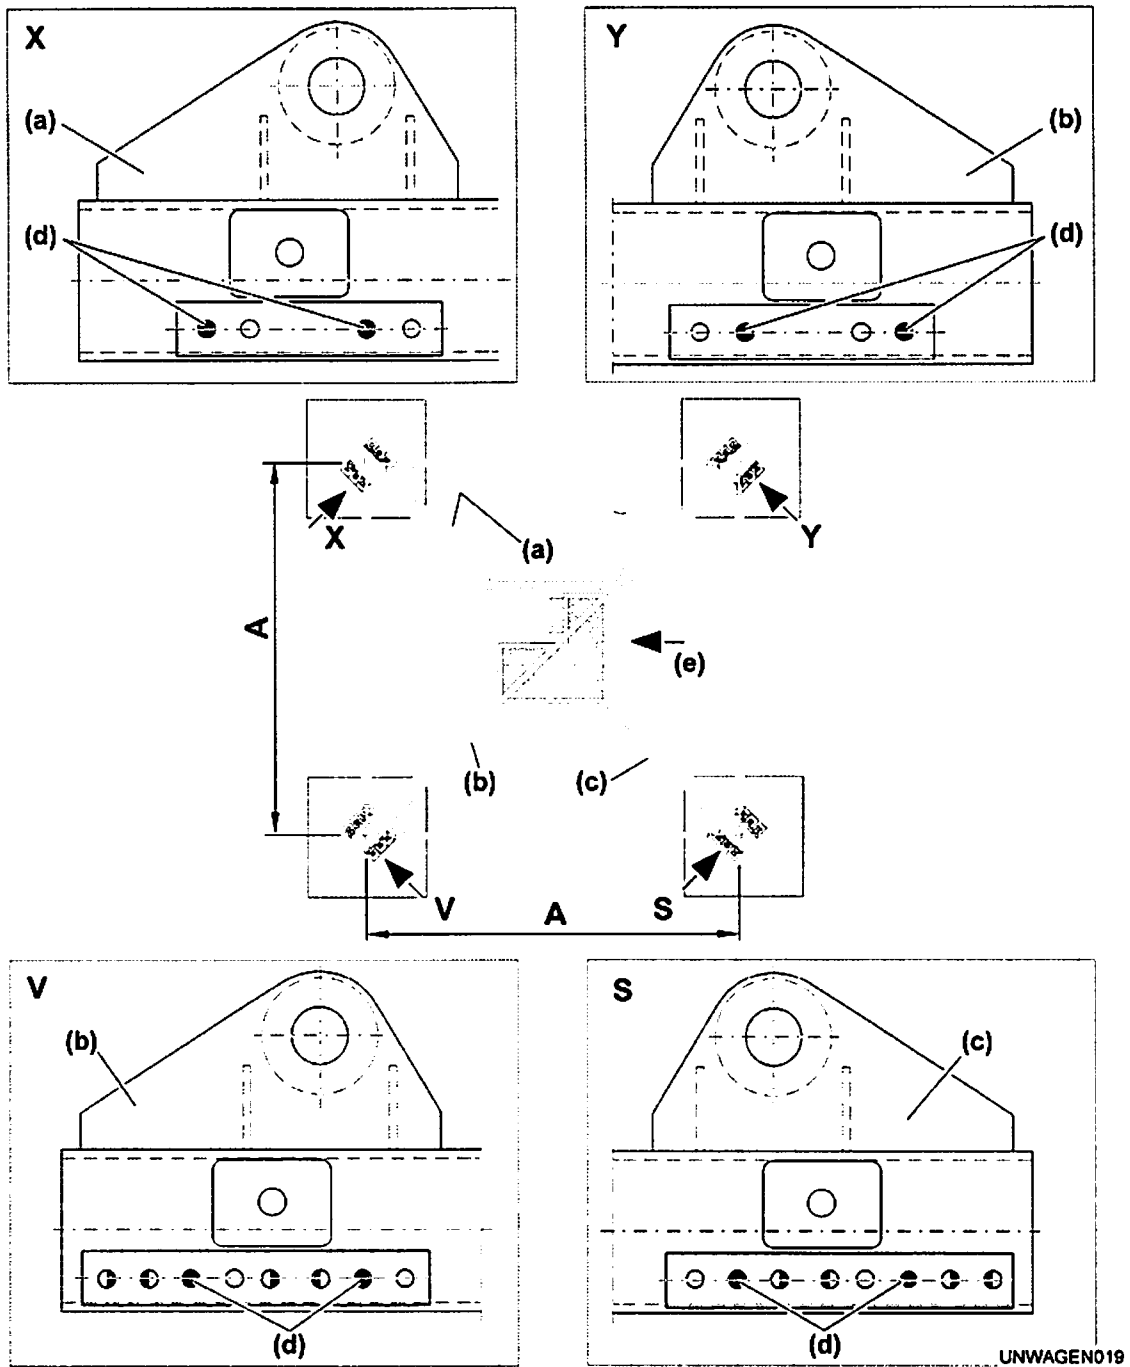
Gewindebohrungen an den Tragholmen des Unterwagens 154 EC-HM oder 140 HC
